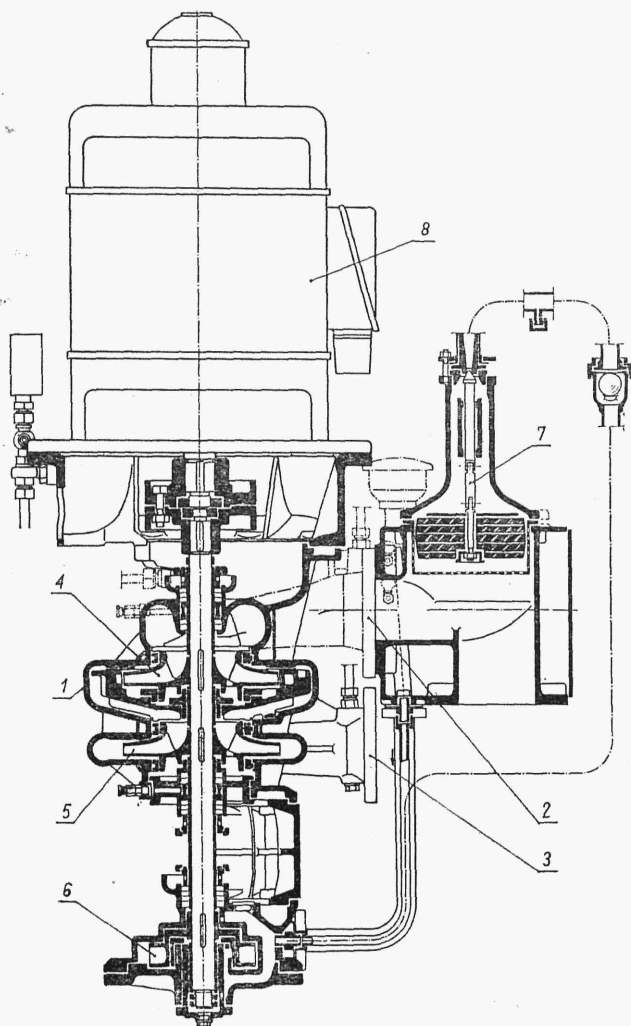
Pompa odśrodkowa pionowa okrętowa typu WPS ze stopniem samozasysającym, produkcji Gliwickiej Fabryki Urządzeń Technicznych; 1 — wirnik główny, 2 — wirnik samozasysający, 3 — kurek sterujący, 4 — kadłub pompy, 5 — silnik elektryczny
